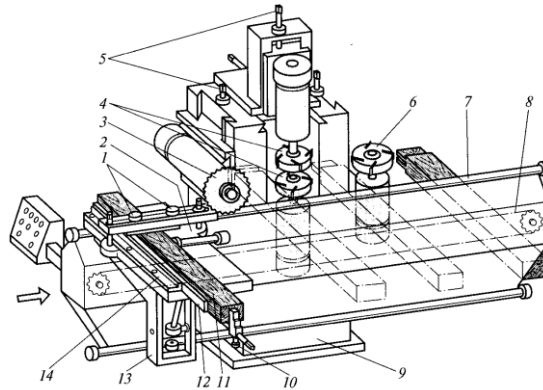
Однобічний рамний шипорізний верстат: 1 – гідропритиски; 2 – стіл; 3 – пила; 4 – шипорізні фрези; 5 – гвинти настроювання; 6 – дискова фреза; 7 – напрямна каретка; 8 – роликотулочний ланцюг; 9 – станина; 10 – упор; 11 – заготівка; 12 – підпирний брусок; 13 – каретка; 14 – напрямна лінійка
